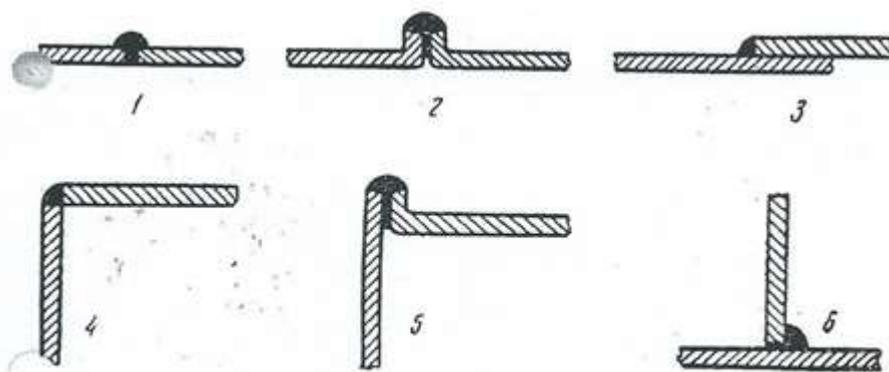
Виды соединений заготовок из тонколистовой стали, выполненных сваркой в углекислом газе.
